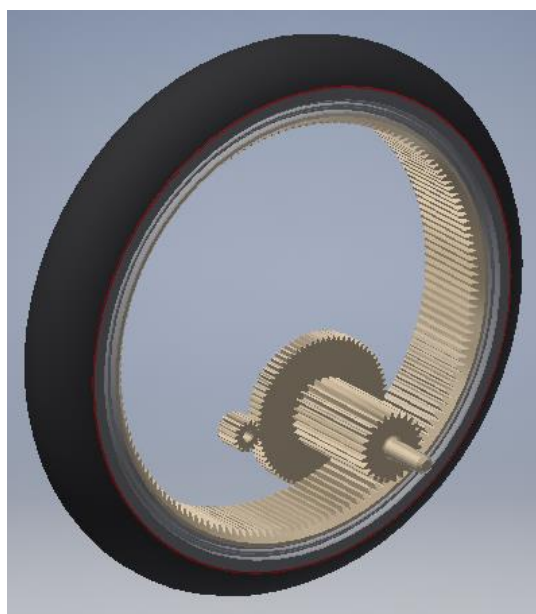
Сборочная 3D-модель зубчатой передачи
